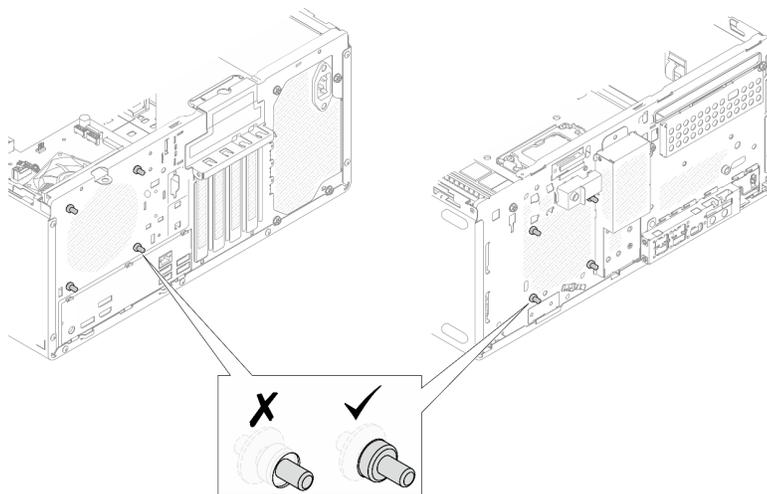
Установка резиновых креплений переднего и заднего вентиляторов
